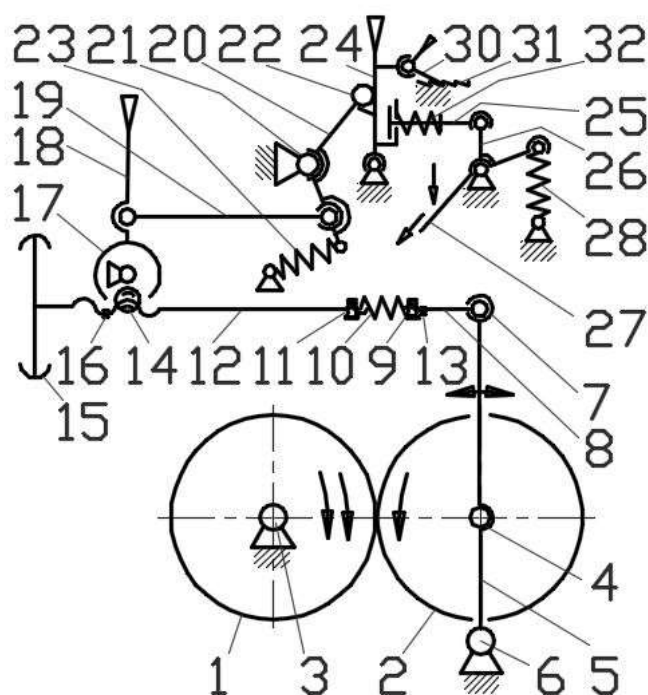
Схема установочного механізму вальцьового верстата ВМП.
